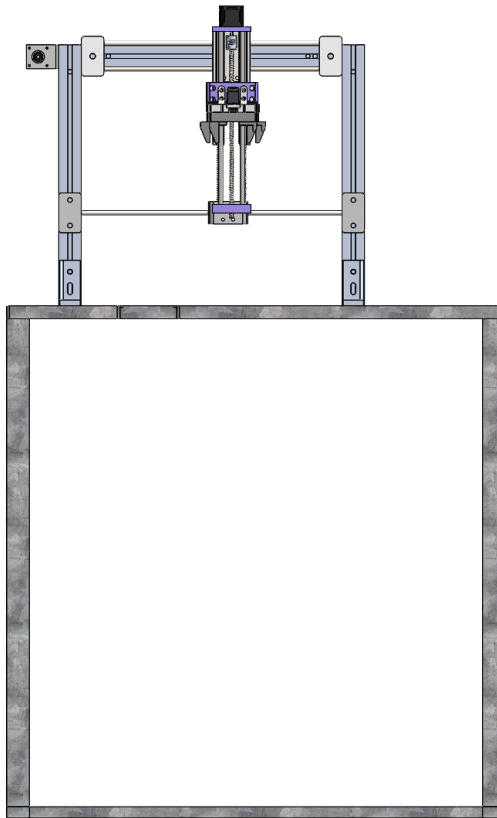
Vista Frontal del Ensamblaje. Fuente: Autores
